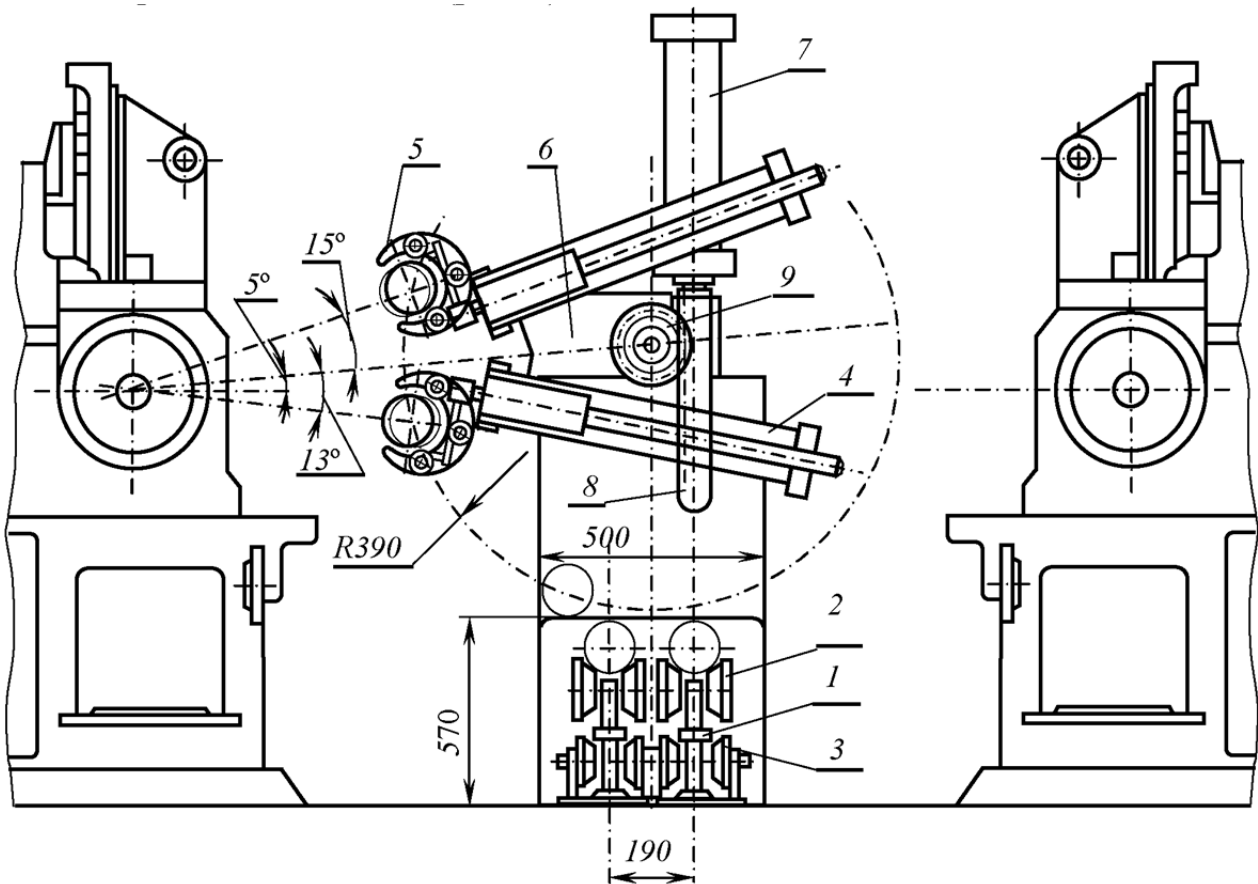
Конструктивная схема автооператора с двумя питателями и закрытыми захватами
